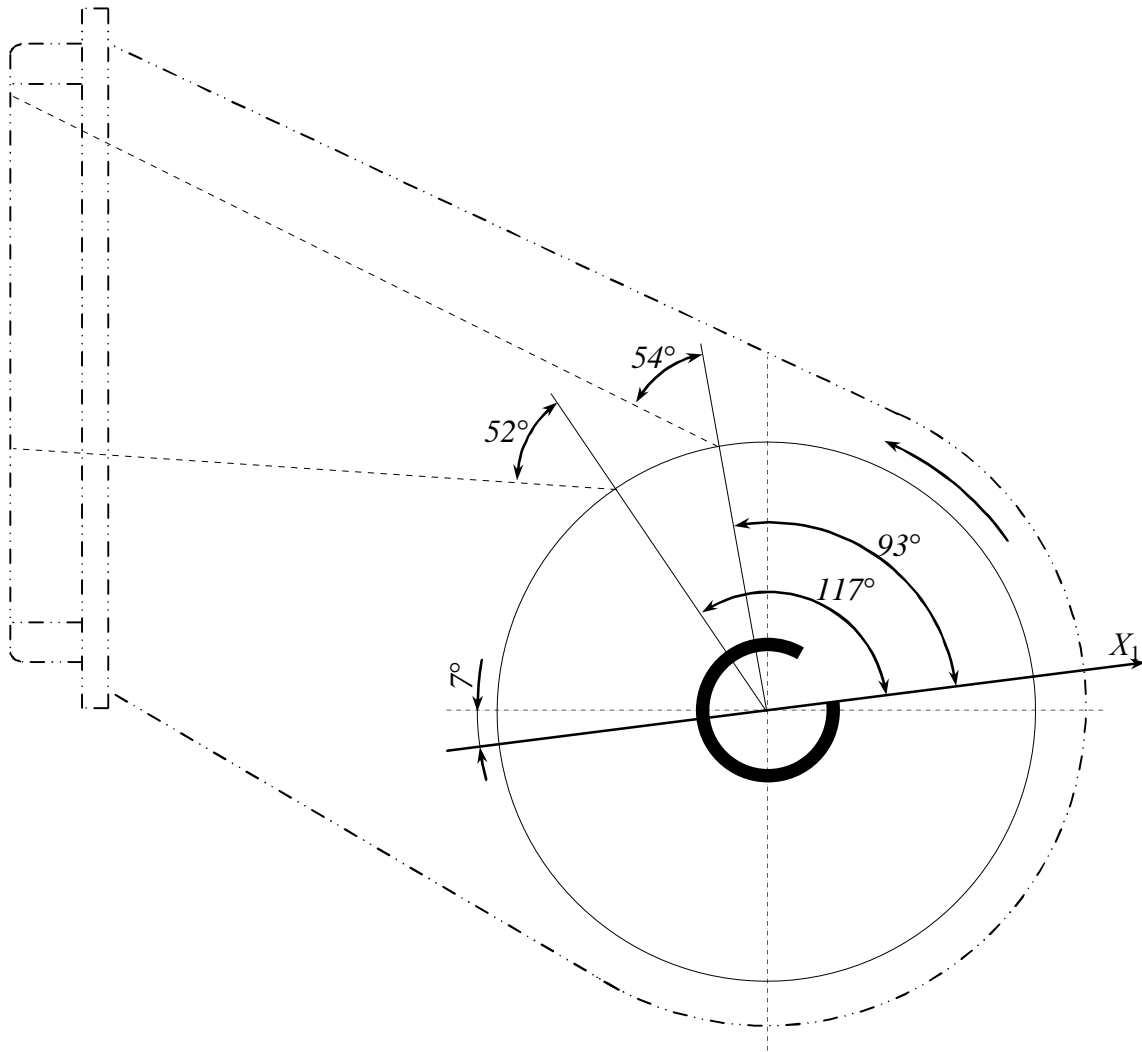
Расчетная схема расположения границ факела предлагаемой конструкции устройства разгона дроби дробебетного аппарата
